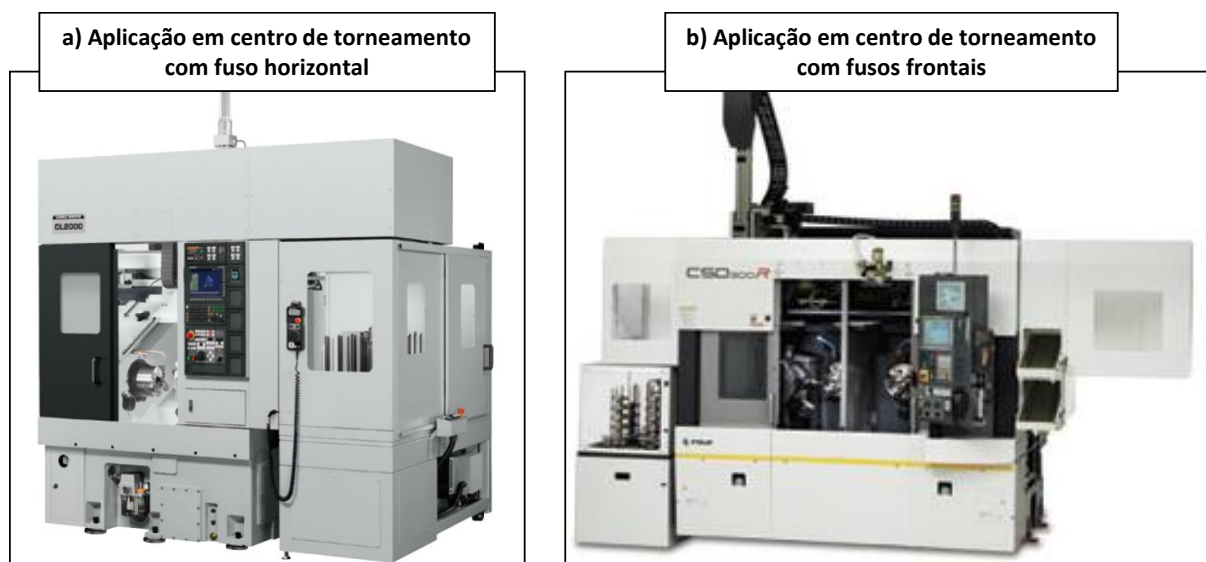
Aplicações de manipuladores pórticos em centros de torneamento: a) com fuso horizontal (DMG MORI, 2017) e b) com fusos frontais (FUJI MACHINES, 2017).
